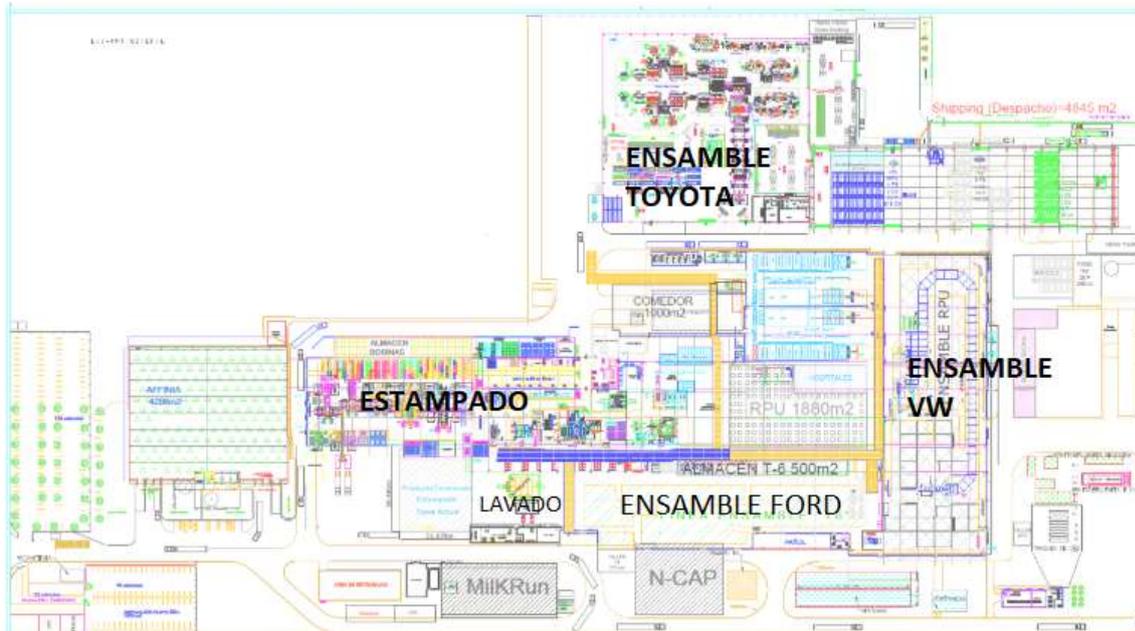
Lay out de la planta. Provisto por Metalsa.
